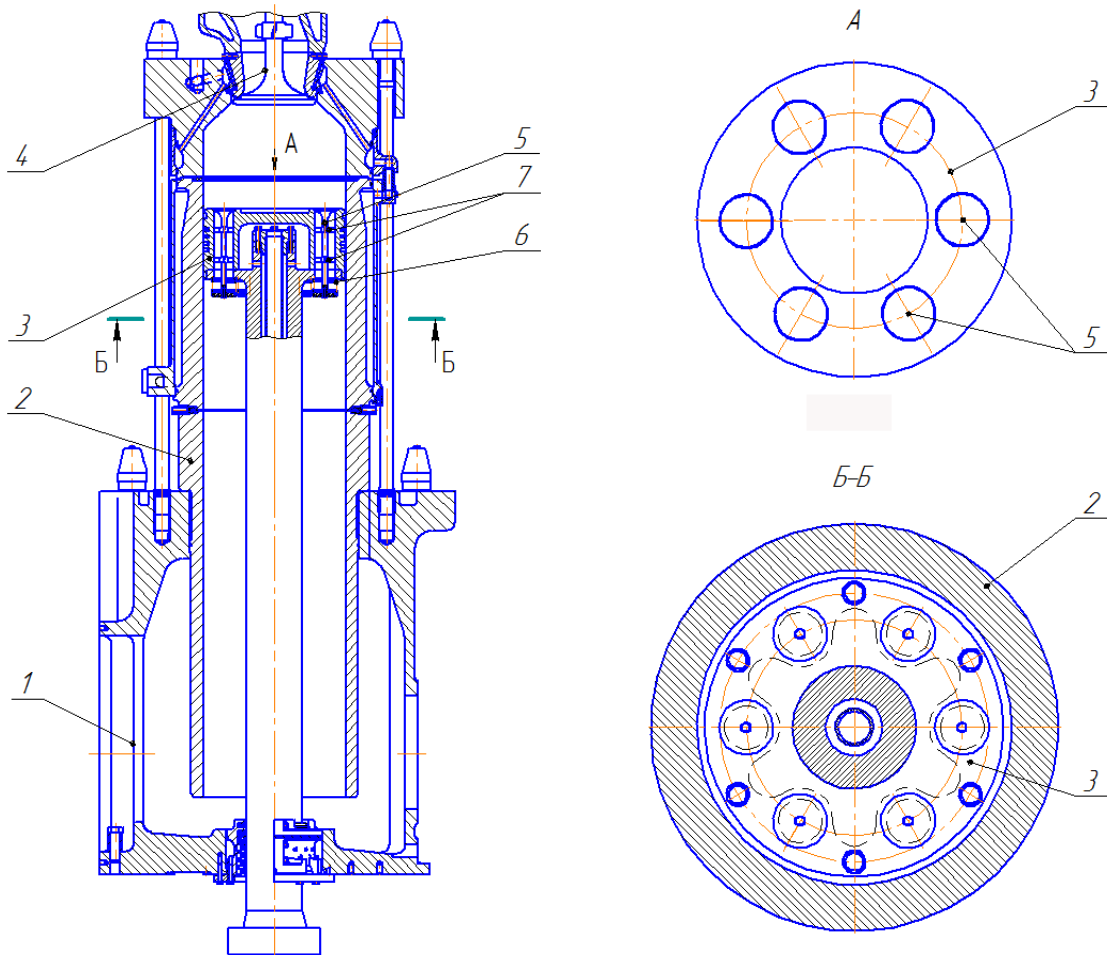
Загальний вигляд прямоточно-клапанної системи газообміну двотактного дизеля: 1 - ресивер продувного повітря; 2 - циліндрова втулка; 3 – поршень; 4 - випускний клапан; 5 - продувні клапани; 6 – пружина; 7 - крилатки
